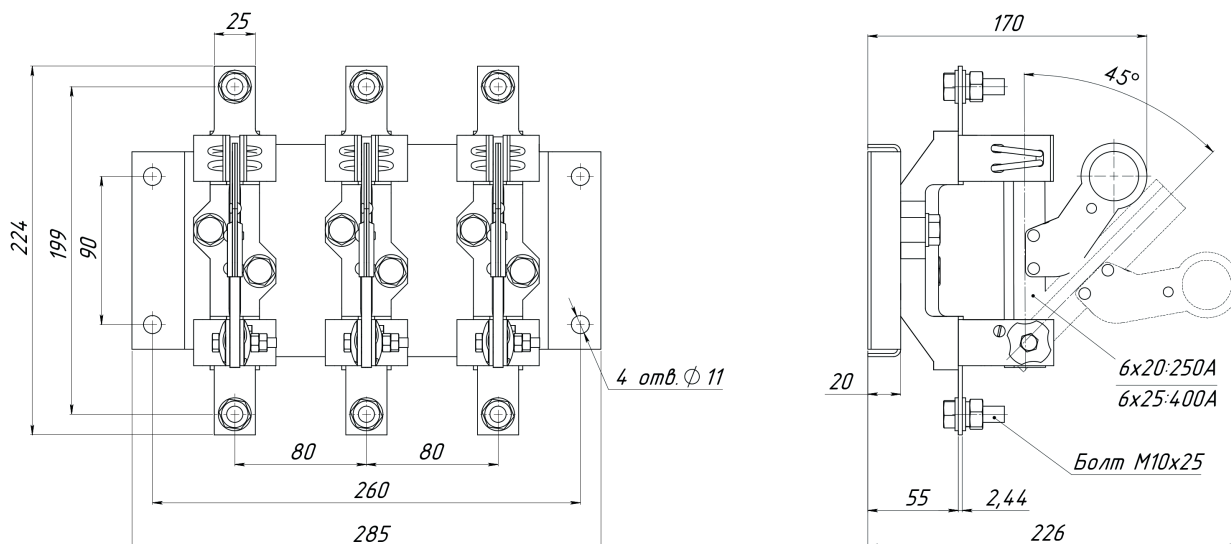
Разъединитель серии Р с полюсным оперированием штангой Р 43, на номинальный ток 250 А и 400 А
